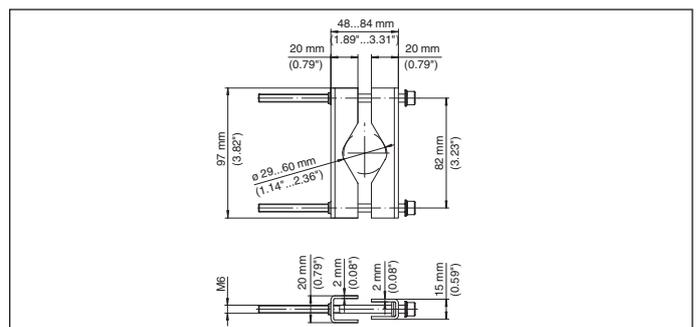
Dimensioni grappe per montaggio su tubo VEGAMET 861, 862
